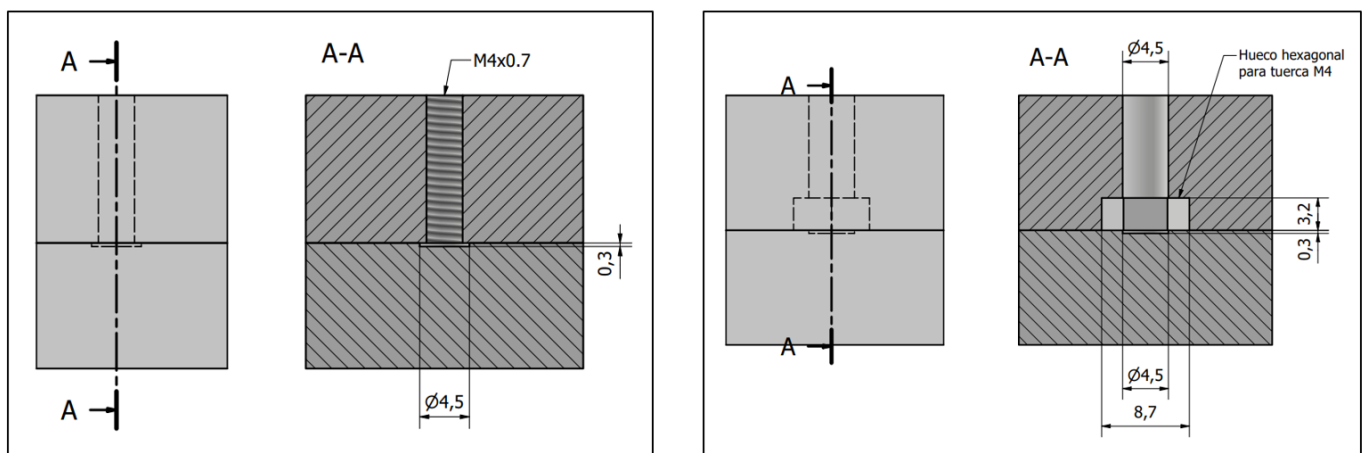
Sistema de desmoldeo aplicado normalmente (*Izquierda*) y sistema de desmoldeo aplicado en el molde impreso (*Derecha*).
